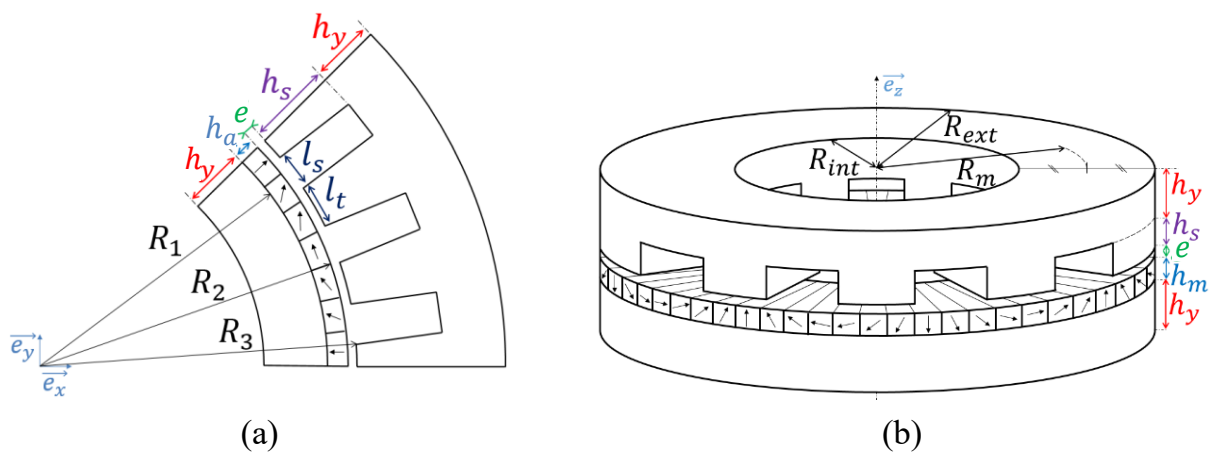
Schémas de la machine à flux radial (a) et flux axial (b) [18]
